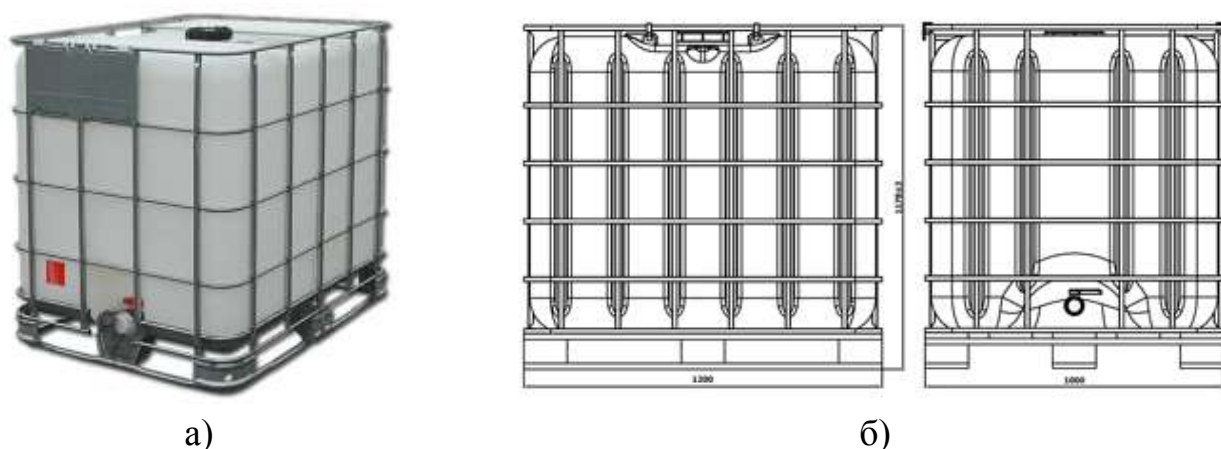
Корпус бака для экспериментальной установки:
